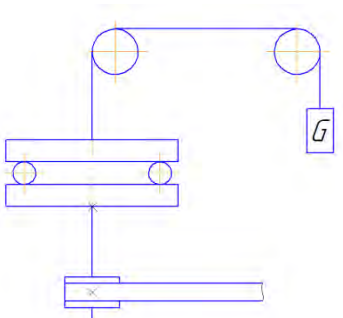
Использование противовеса в конструкции шарообрабатывающего станка
